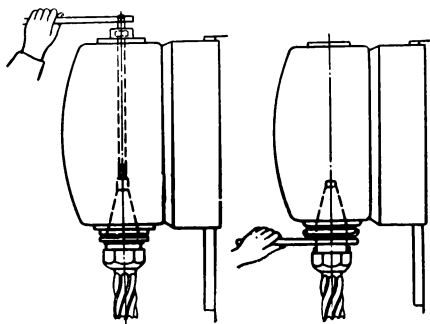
Сопоставление крепления фрезы при помощи шомпола и при помощи быстродействующего патрона
